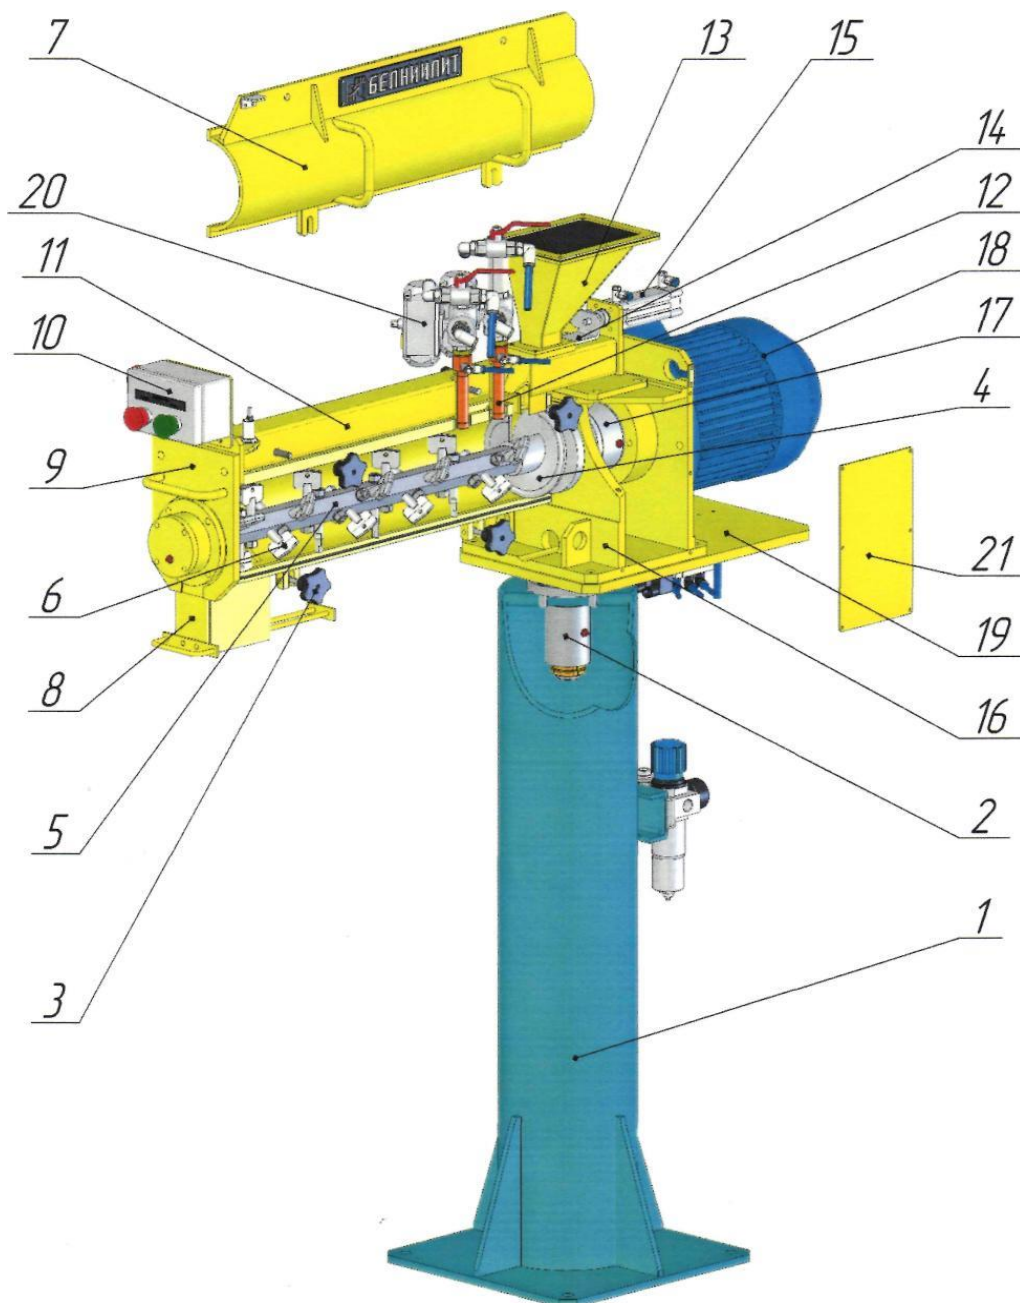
Загальний вид змішуючого агрегату, встановленого на опорну колону:
